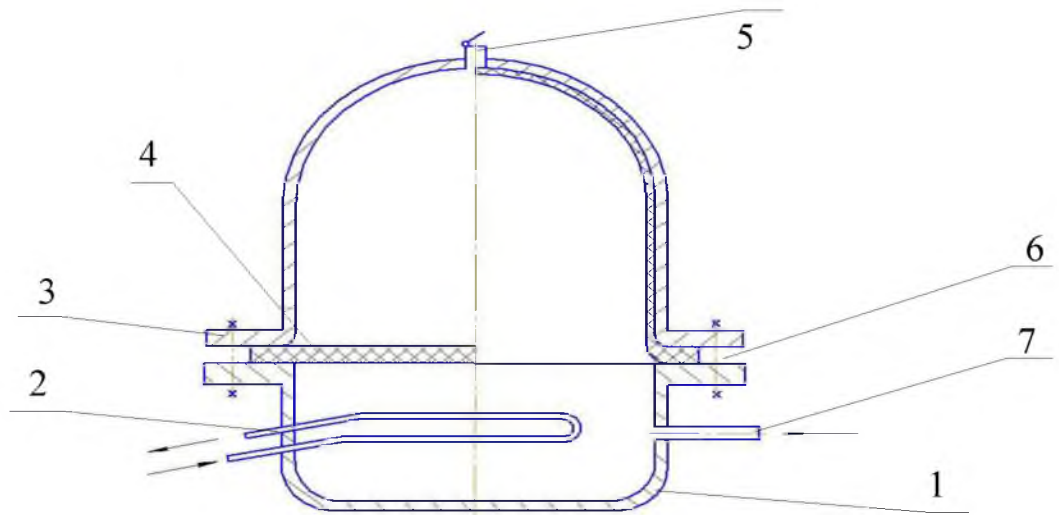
Схема вакуумної камери: 1- камера-ресивер; 2 - патрубок - розпилювач пари; 3 - камера; 4 - мембрана; 5 - клапан для стравлення повітря; 6 - кріплення; 7 - патрубок для всмоктування небезпечних речовин
